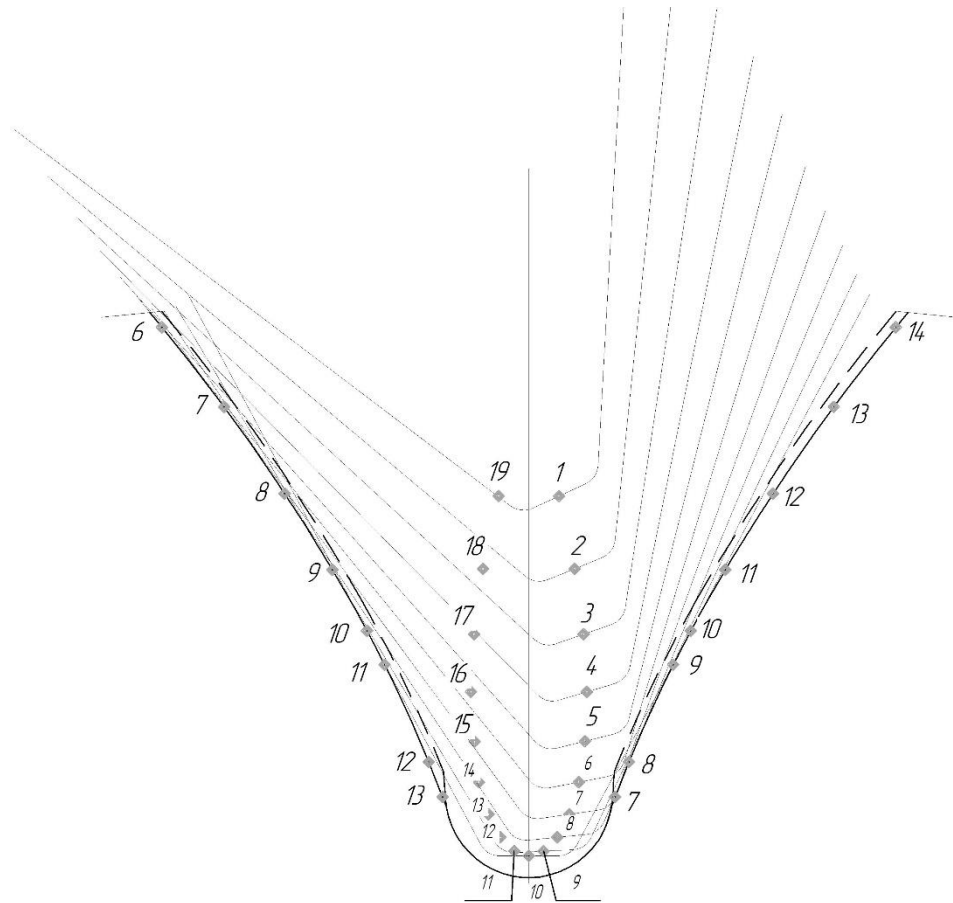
Схема процесса формирования профиля зуба при зубошлифовании червячным кругом
